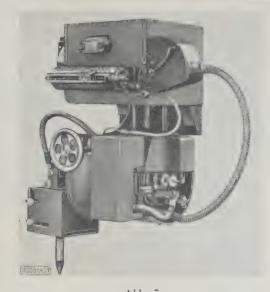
Schweißkopf für Drahtschweißung mit Lichtbogen-Ziehspule der Firma Elin, Weiz, Steiermark.
